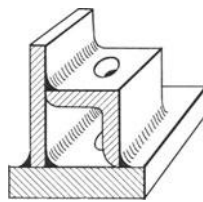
Schraubenansatz an Maschinenständern und Stützen.
